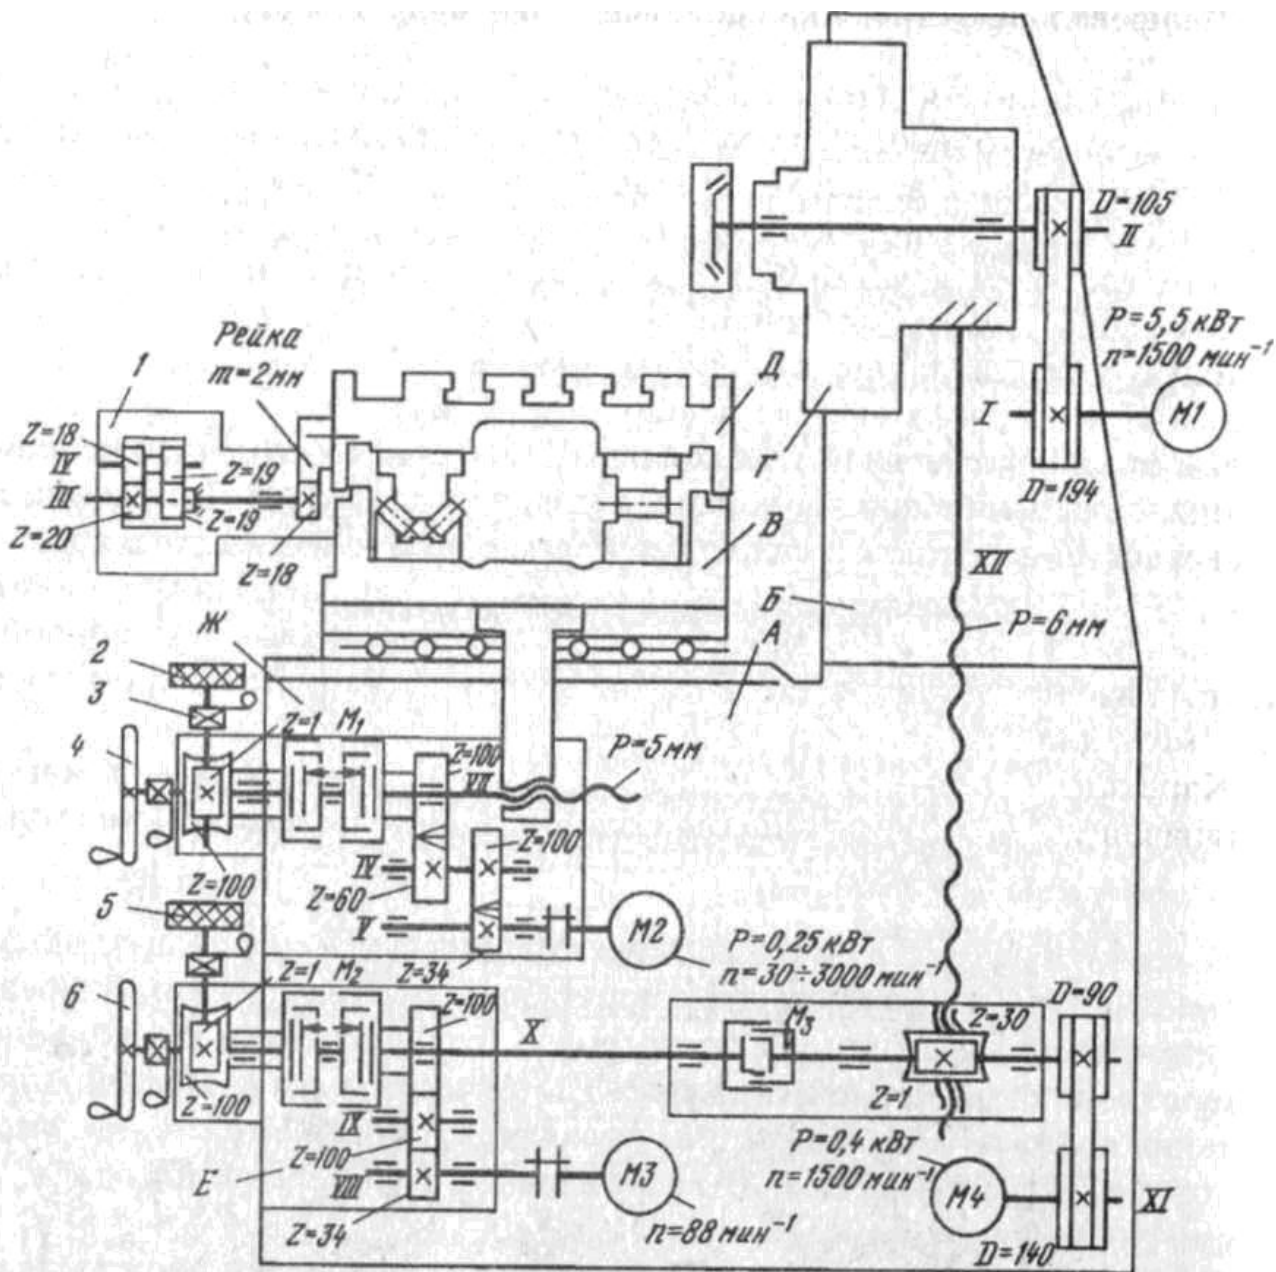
Кинематическая схема плоскошлифовального станка модели 3E711B: А – станина, Б – колонна, В – крестовый суппорт, Г – шлифовальная головка, Д – стол, Е, Ж – механизмы вертикальной и поперечной подачи.
